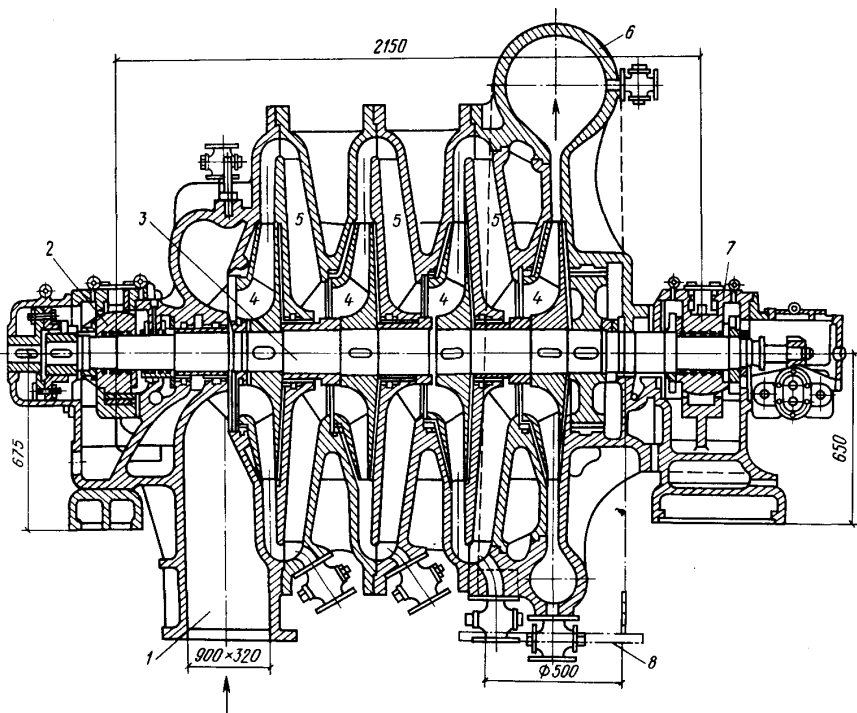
Турбовоздуходувка: 1 – входной патрубок; 2 – опорный подшипник; 3 – вал; 4 – рабочие колеса; 5 – конфузор; 6 – выходной патрубок; 7 – опорно-упорный подшипник; 8 – разгрузочная труба
